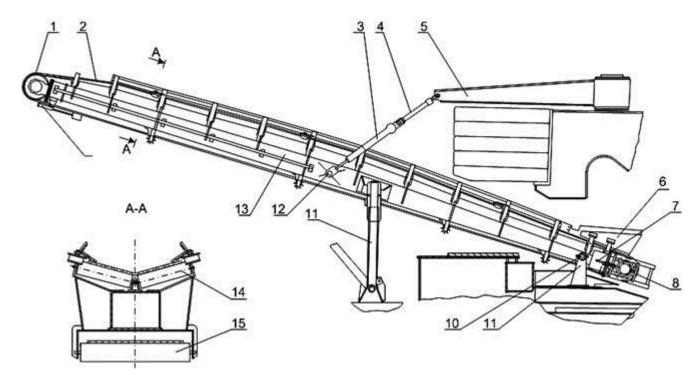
Конвейер поворотный: 1- барабан оборотный; 2- лента; 3- подвеска; 4- гидроцилиндр; 5- поворотная стрела; 6- загрузочная воронка; 7- натяжное устройство; 8- барабан приводной; 9- опора поворотного механизма; 10, 12- оси; 11- откидная стойка; 13- каркас; 14- ролик направляющий; 15- ролик очистительный
